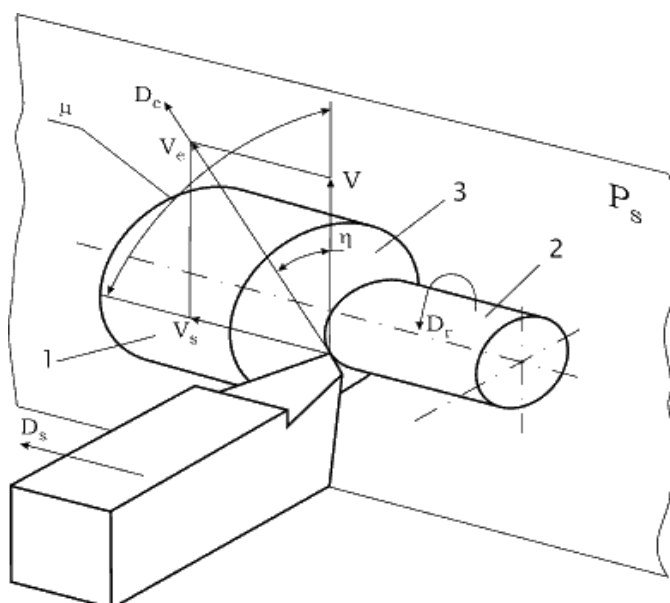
Поверхности и движения при резании: 1 – обрабатываемая поверхность; 2 — обработанная поверхность; 3 – поверхность резания; P_s – рабочая плоскость; V – вектор скорости резания; V_s – вектор скорости движения подачи; V_e – вектор скорости результирующего движения; D_r – главное движение; D_s – движение подачи; D_e – результирующее движение.
